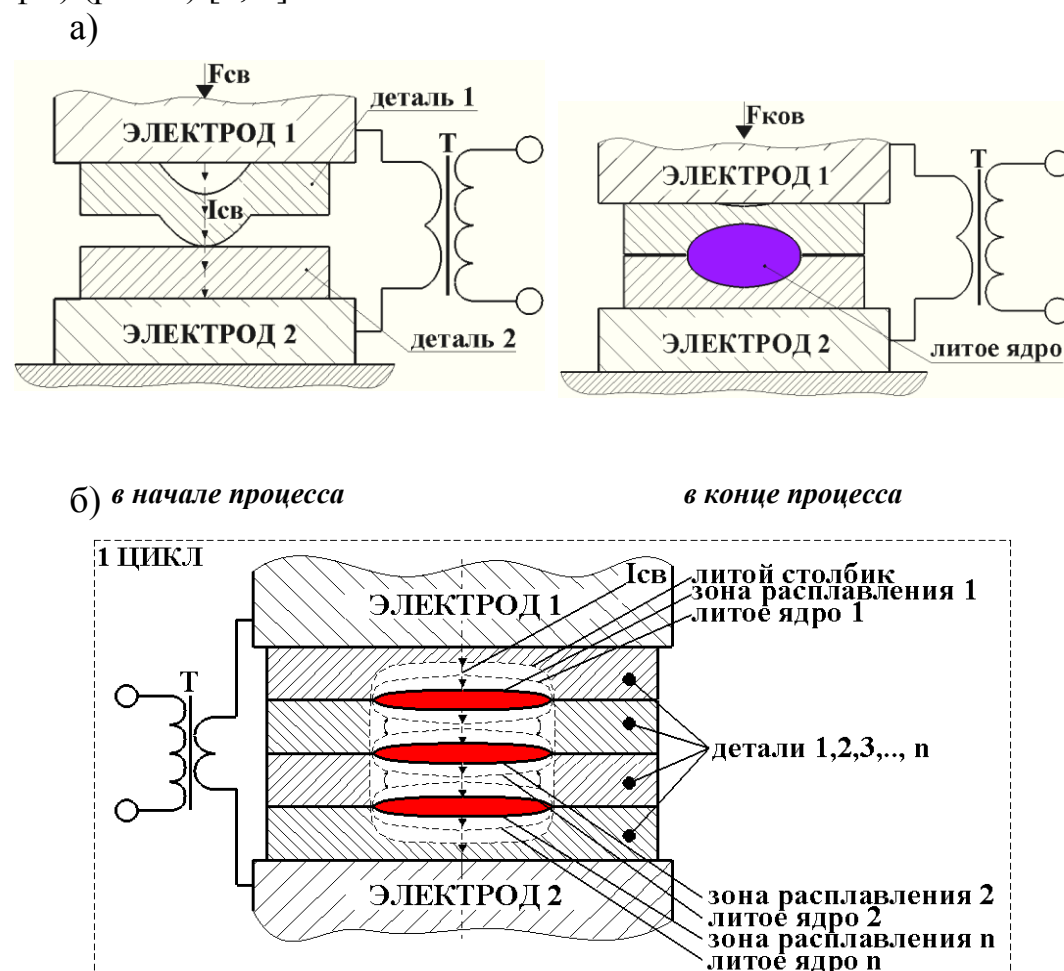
Схема процесса КРС нахлесточного соединения, состоящего из двух (а) и четырех деталей (б): Т – сварочный трансформатор; $I_{св}$ – сварочный ток; $F_{св}$ – усилие сжатия электродов; $F_{ков}$ – ковочное усилие
